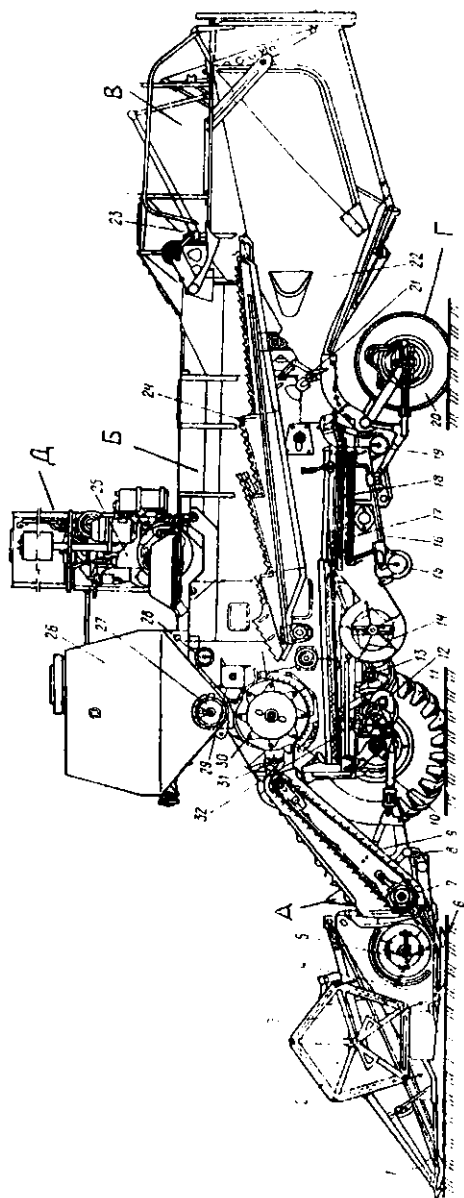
Зерноуборочный комбайн СК-5 "Нива" 1-делитель; 2-моторило; 3-режущий аппарат; 4-корпус жатки; 5-шнек; 6-копирующий башмак; 7-цепочно-планчатый плавающий транспортер; 8-центральный шарнир подвески корпуса жатки; 9-наклонный корпус; 10-гидроцилиндр подъема жатки; 11-ведущее колесо; 12-коробка передач моста ведущих колес; 13-вал привода транспортной доски; 14- вентилятор; 15- зерновой шнек; 16-решетный стан; 17- нижнее жалюзийное решето; 18-верхнее жалюзийное решето; 19-колосовой шнек; 20-управляемое колесо; 21- половонабиватель копнителя; 22- копнитель; 23- соломонабиватель; 24-клавишный соломотряс сепаратор; 25-двигатель; 26-бункер для зерна; 27- выгрузной шнек; 28-верхний колосовой шнек; 29-отбойный битер; 30-мологильный аппарат; 31- приёмный битер; 32-транспортная доска.
